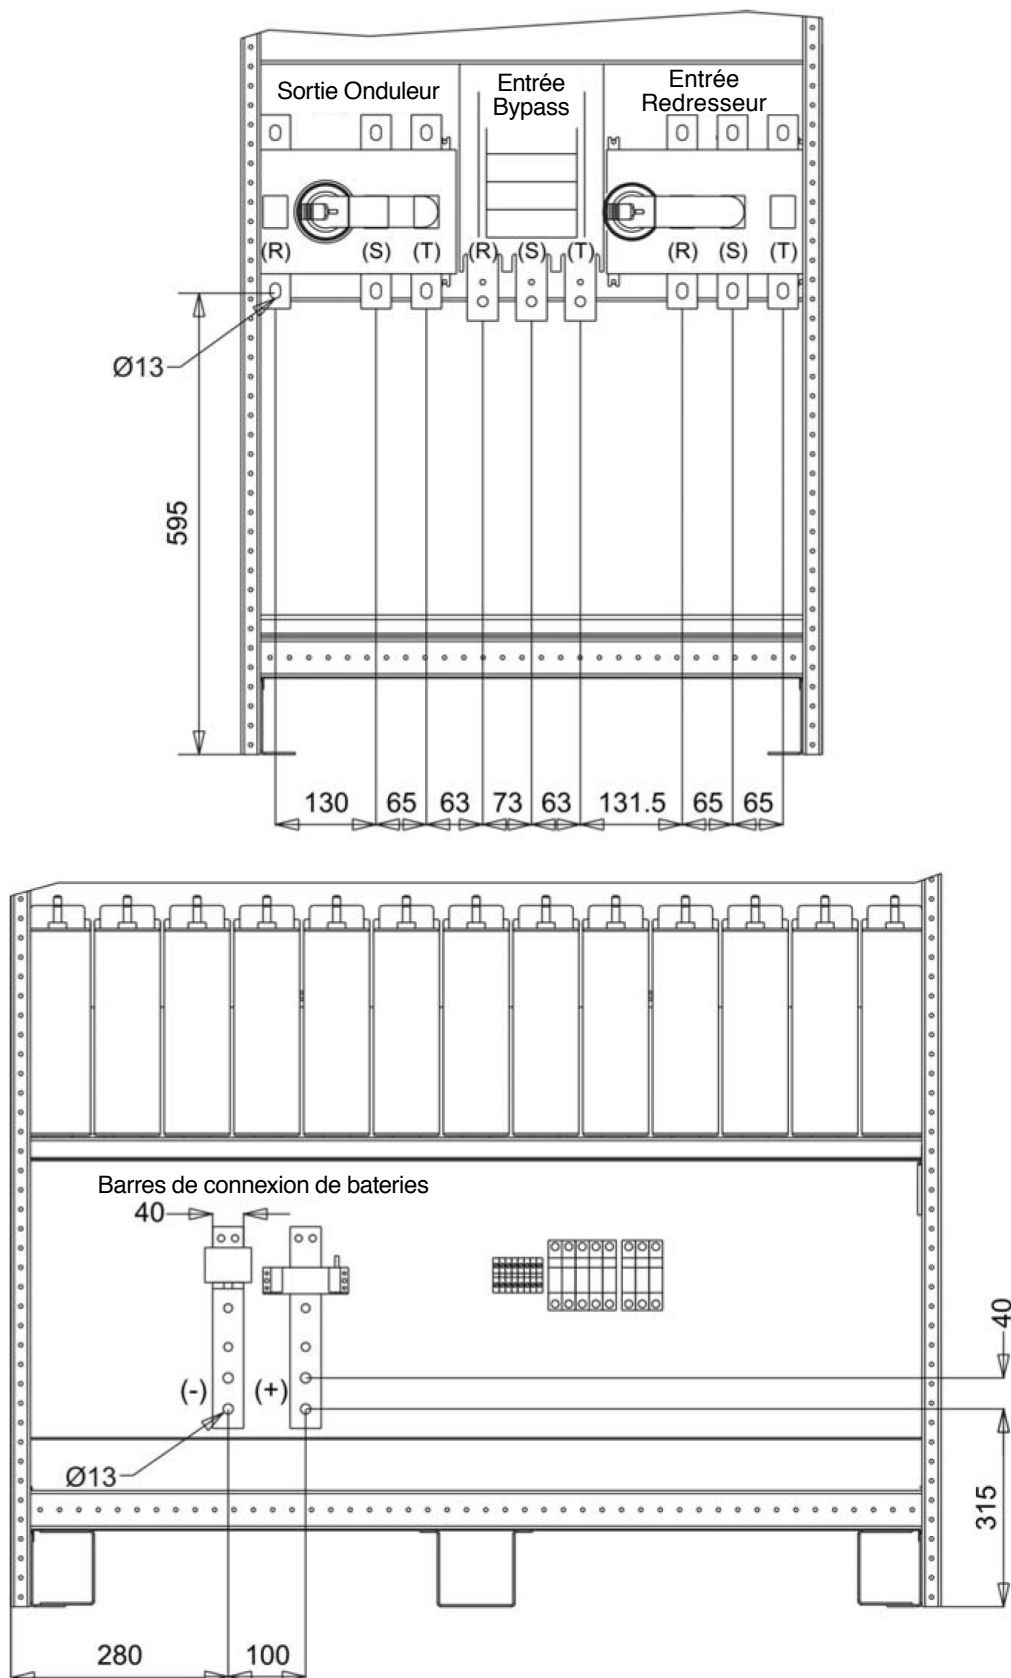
Disposition bornes ONDULEUR 400 kVA (vue frontale)
